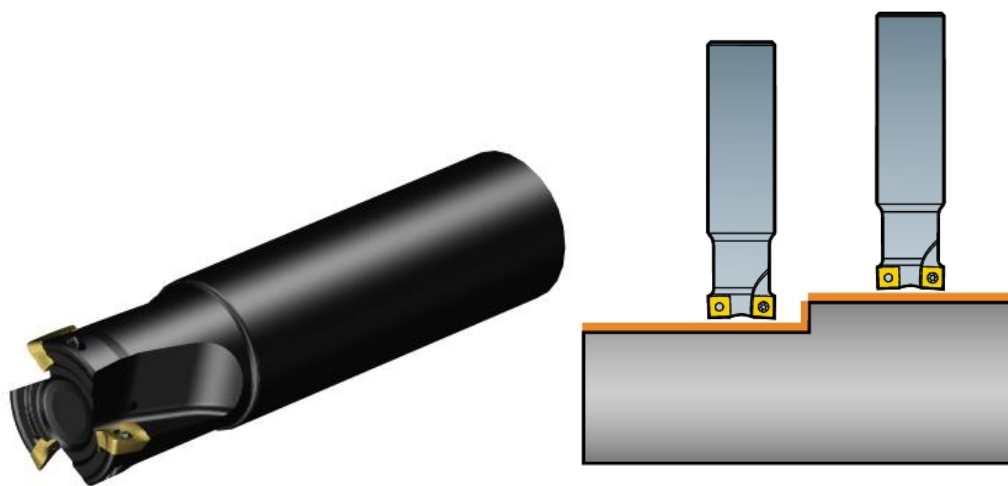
Концевая фреза со сменными многогранными пластинами
